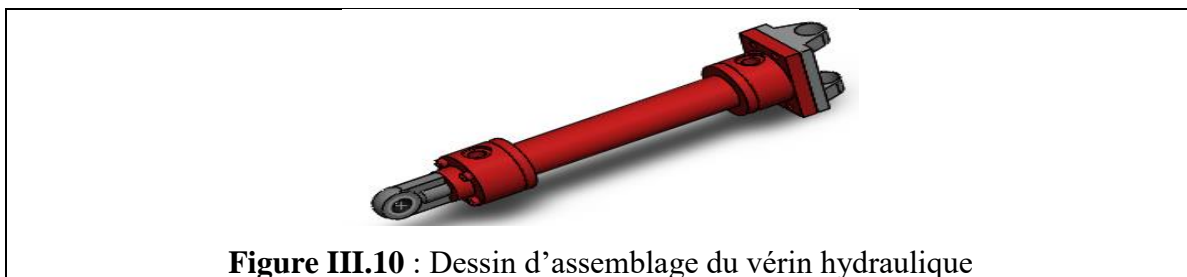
Dessin d'assemblage du vérin hydraulique
